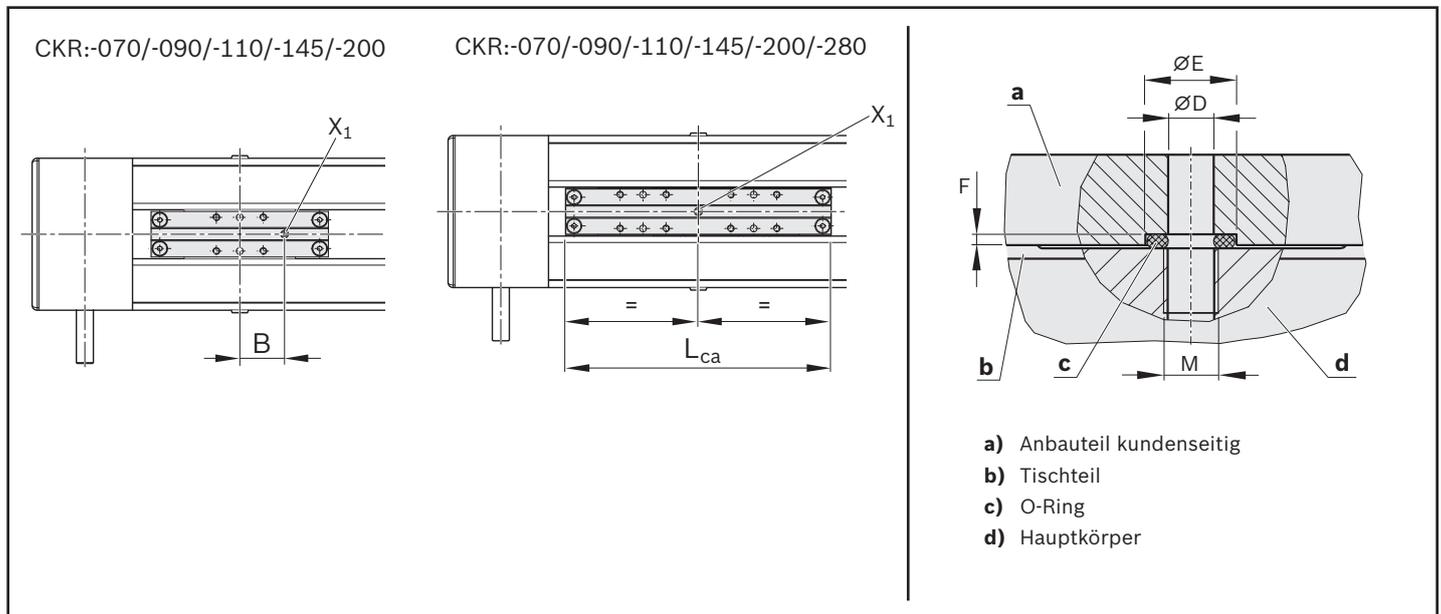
Lage der Schmierbohrungen im Tischteil (CKR)
